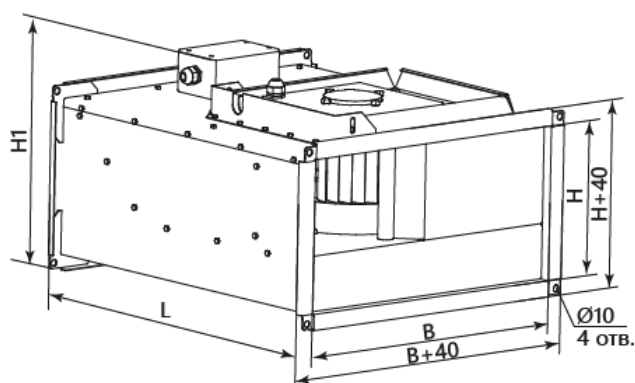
Габаритные установочные и присоединительные размеры вентиляторов
